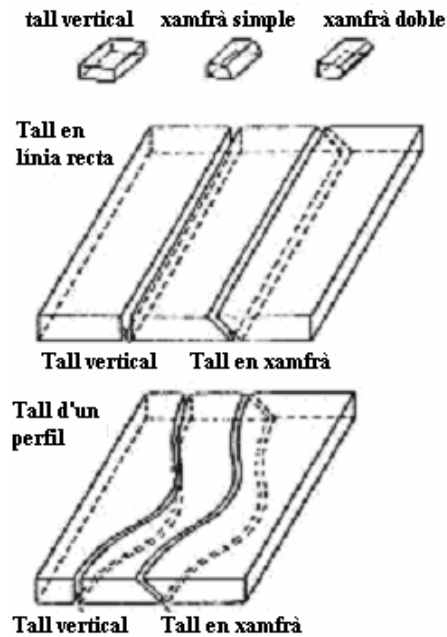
Preparació de xamfrans o juntes per a soldadura
